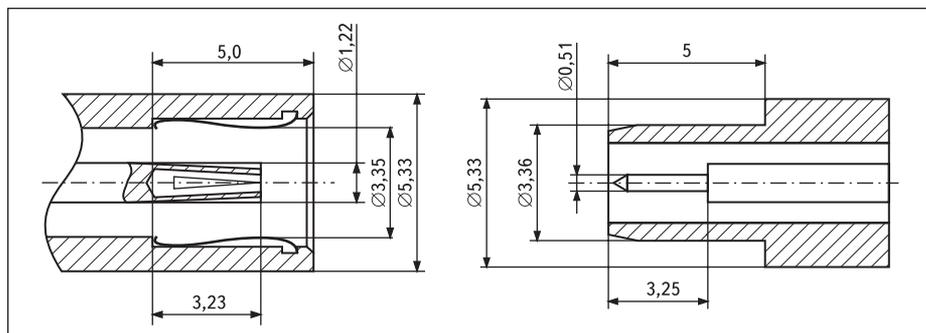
Соединители OSSP: а) розетка; б) вилка
